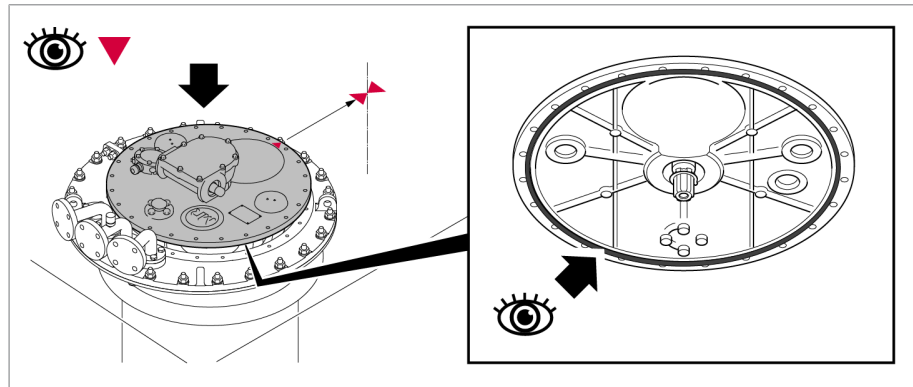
Laststufenschalterkopfdeckel mit O-Ring
